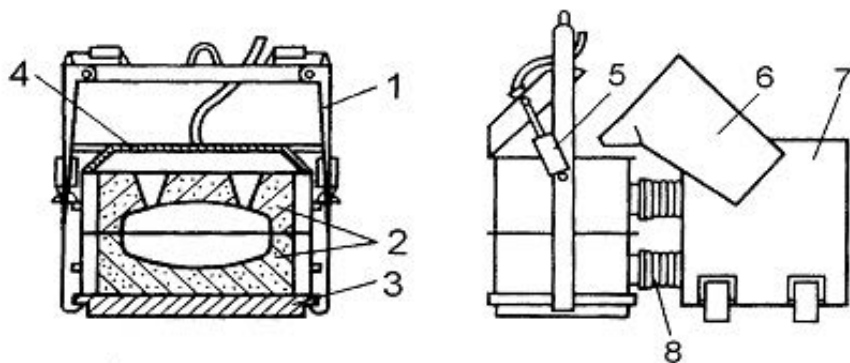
Схема устройства для создания повышенного давления на песчаную форму: 1 – элемент подвесного контейнера; 2 – полуформы; 3 – транспортная плита; 4 – герметизирующая крышка; 5 – привод; 6 – ковш; 7 – заливочная машина; 8 – клапаны
